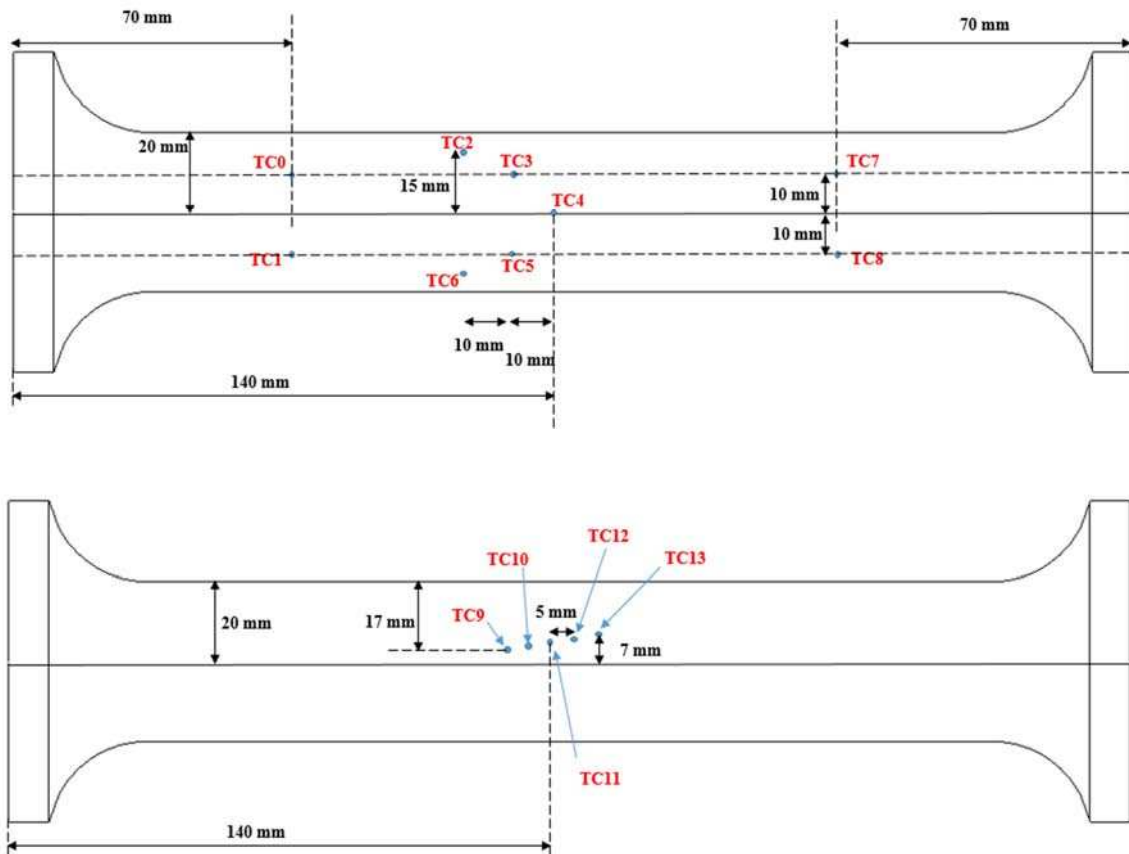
Plan des thermocouples installés sur la face envers (haut) et endroit (bas)
